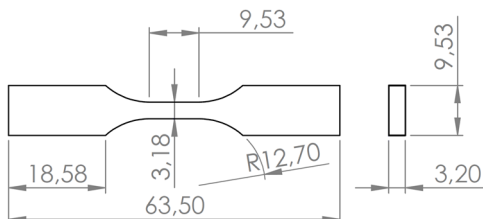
Geometria com dimensões em mm do corpo de prova da norma ASTM D638.
